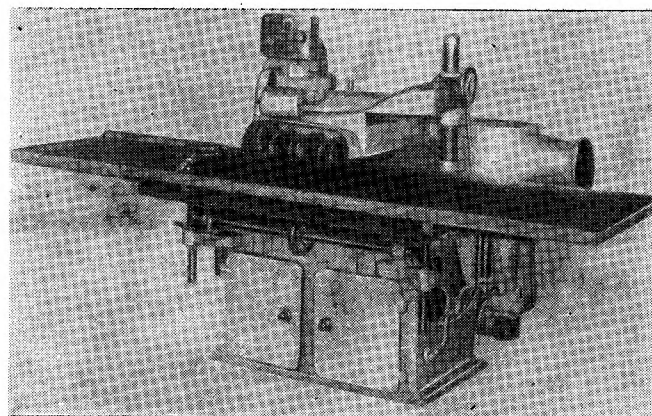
Кромкошлифовальный станок ШЛНСВ
